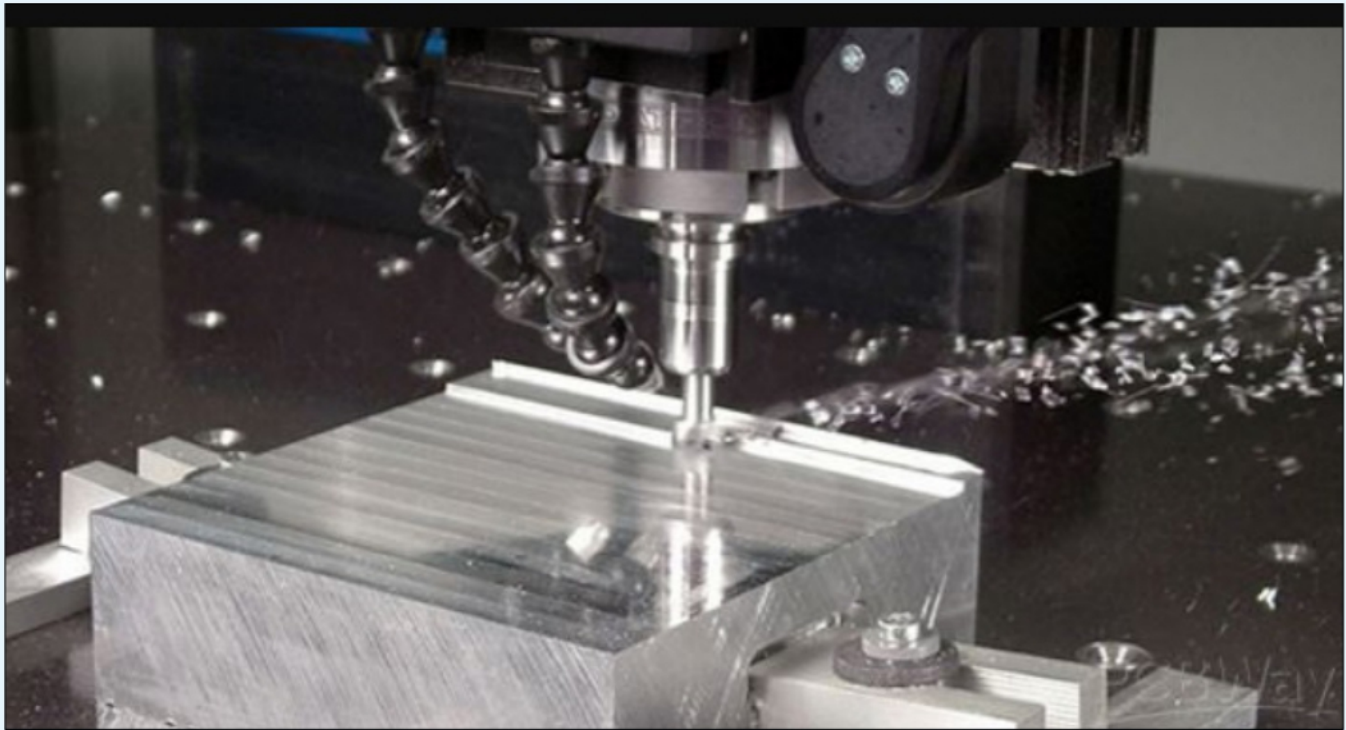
Fresatrice CNC di PCBWay in opera (PCBWay)
